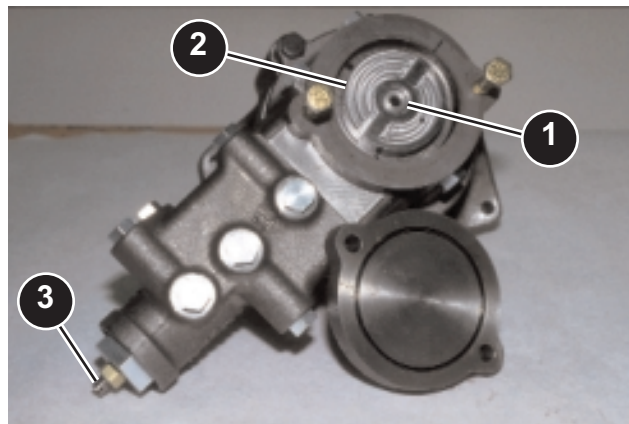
Válvula piloto de dirección fuera de la máquina
